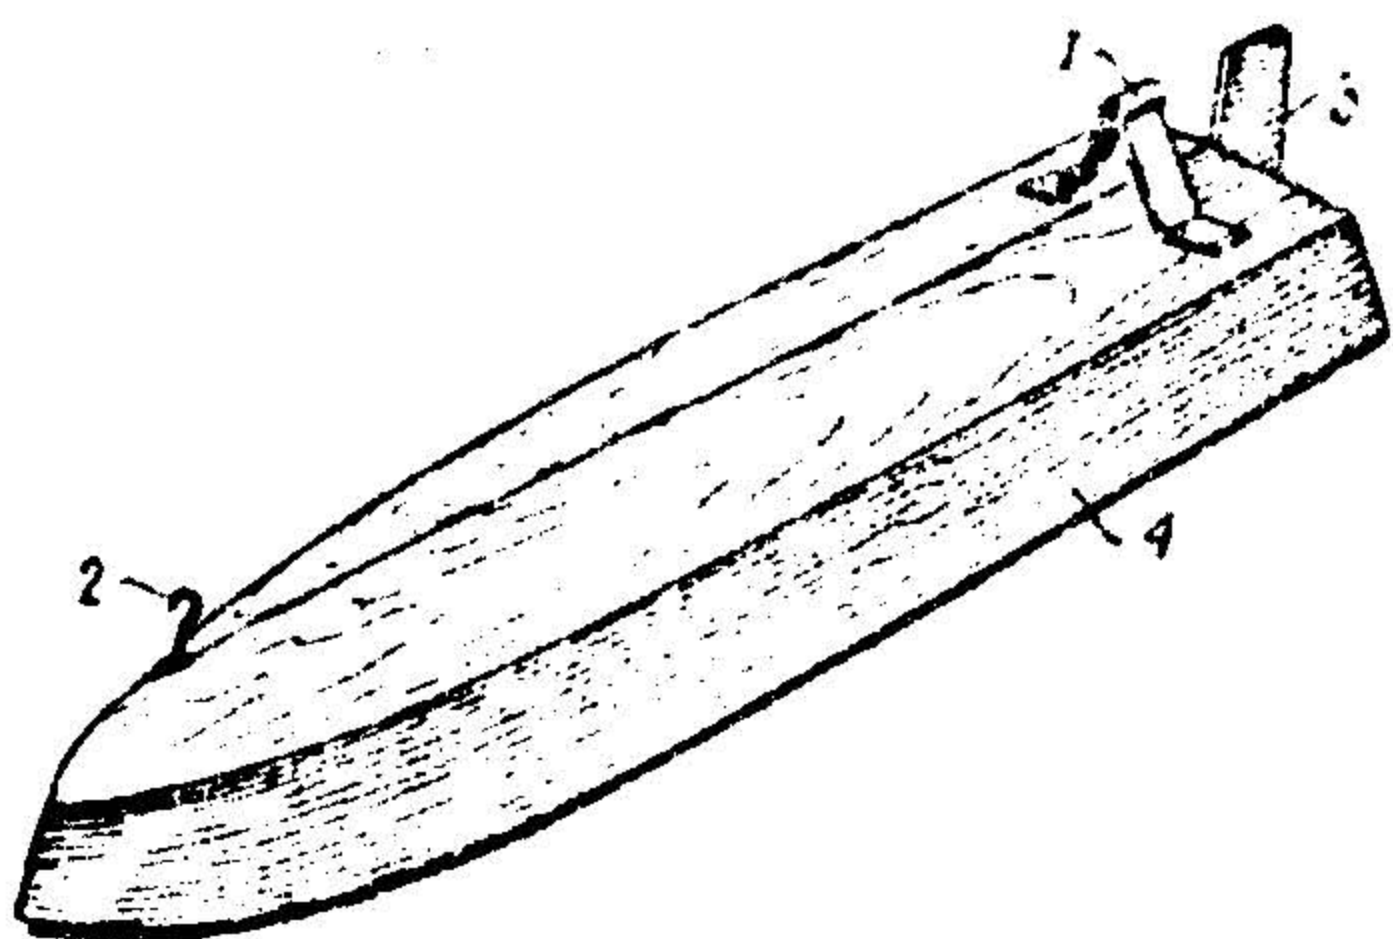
Установка деталей корпуса: 1 — кронштейн; 2 — крючок; 3 — руль; 4 — корпус модели
